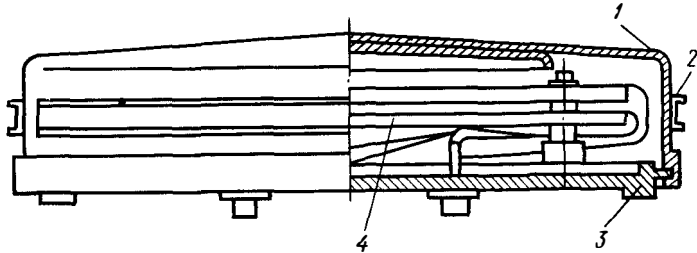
Блок РЭС с кожухом штамповсварной конструкции:
